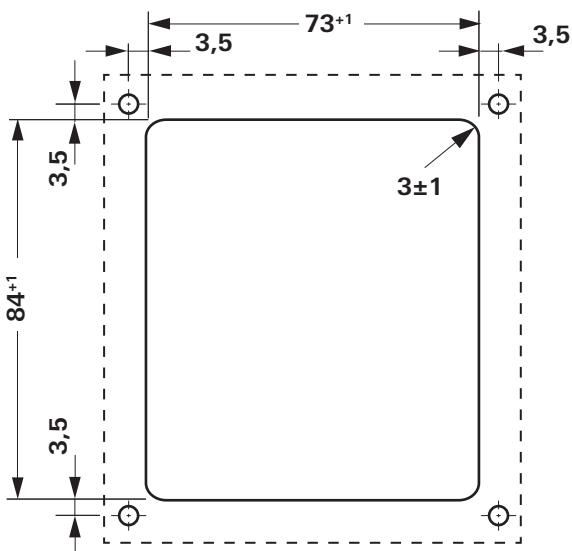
Rozměry v mm. Zobrazení není v přesném měřítku
